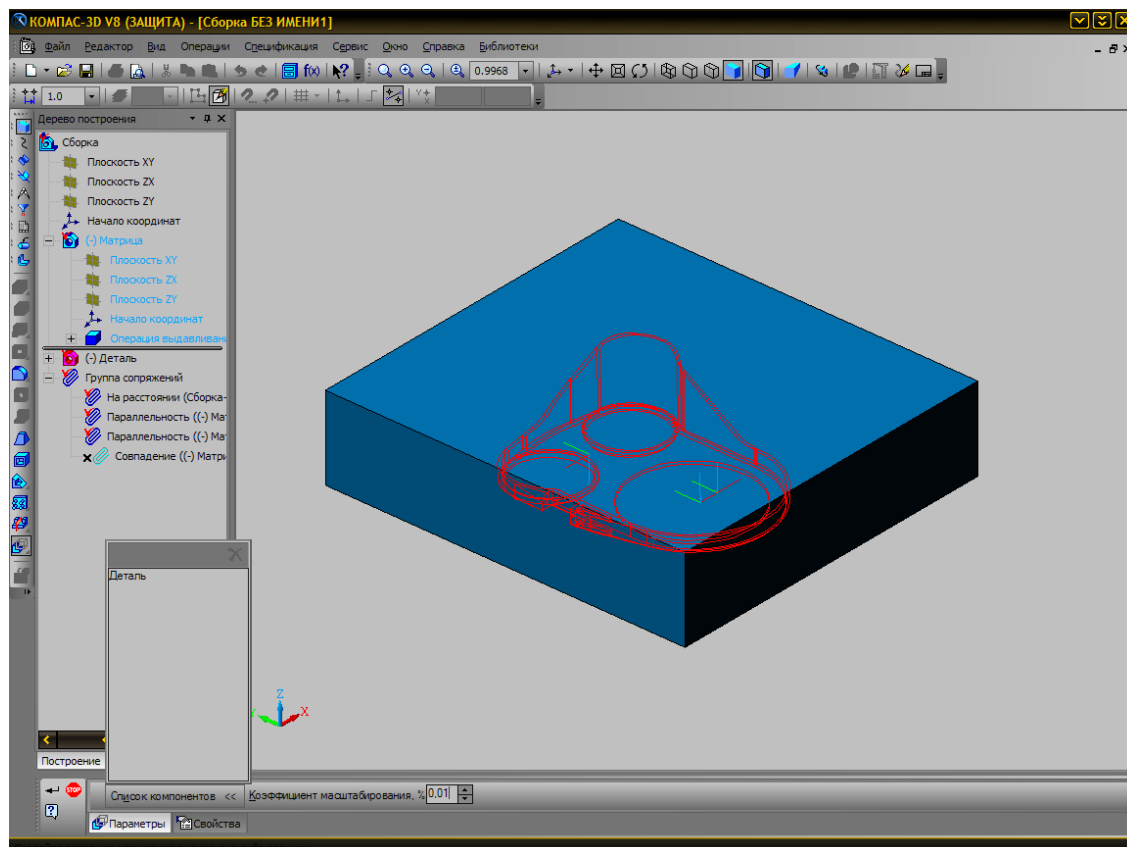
Вычитание детали из матрицы для получения активных поверхностей
